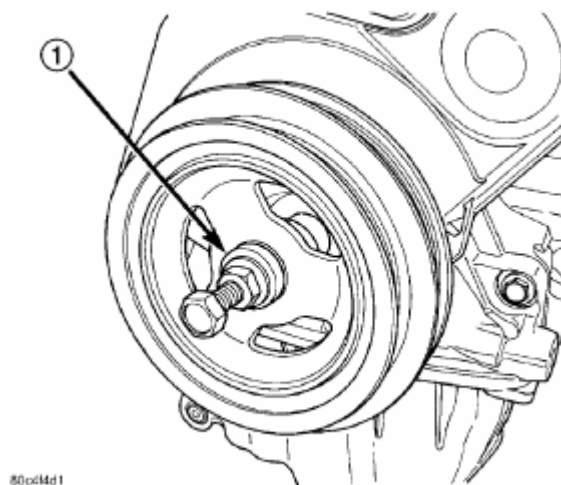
Гаситель вибрации коленчатого вала – типовая установка.
